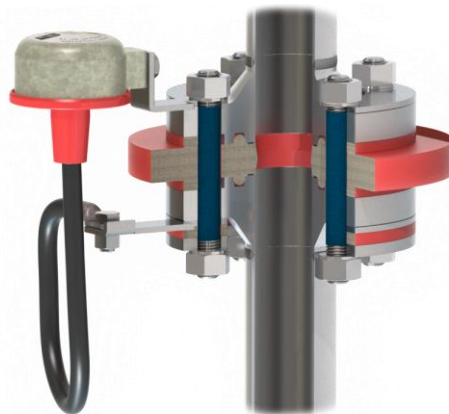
komplett ausgerüstete Isolierflanschverbindung mit Schutz vor unbeabsichtigter Überbrückung, Funkenschutz und Erdung der Schrauben
